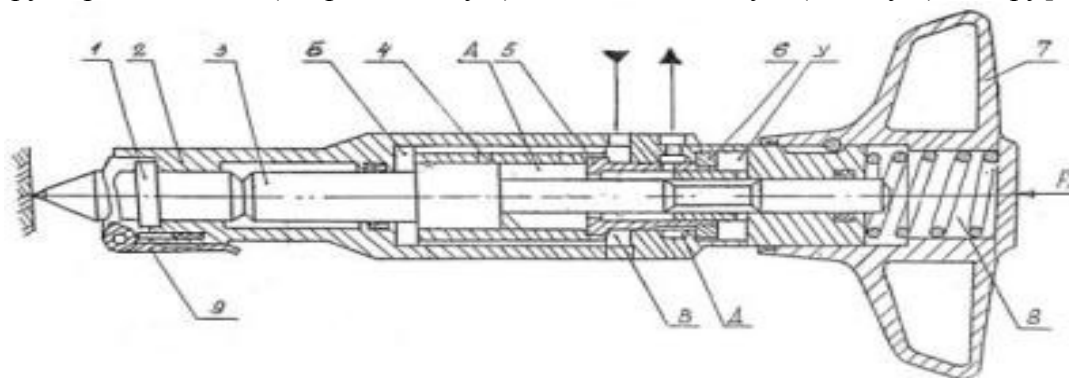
Ручная ударная машина с гидравлическим ударным механизмом: 1-инструмент; 2 - корпус; 3 - поршень-ударник; 4 - отверстие запуска; 5 - клапан; 6 - втулка; 7 - рукоятка; 8 – пружинно-воздушный аккумулятор; 9 - держатель инструмента; А, Б, В, Д, У - камеры: соответственно рабочего и обратного ходов поршня – ударника; вспомогательная; дроссельная; управления.
